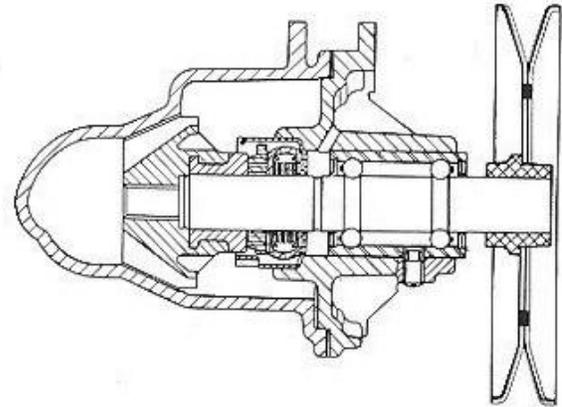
Längsschnitt durch die Kühlwasserpumpe.
